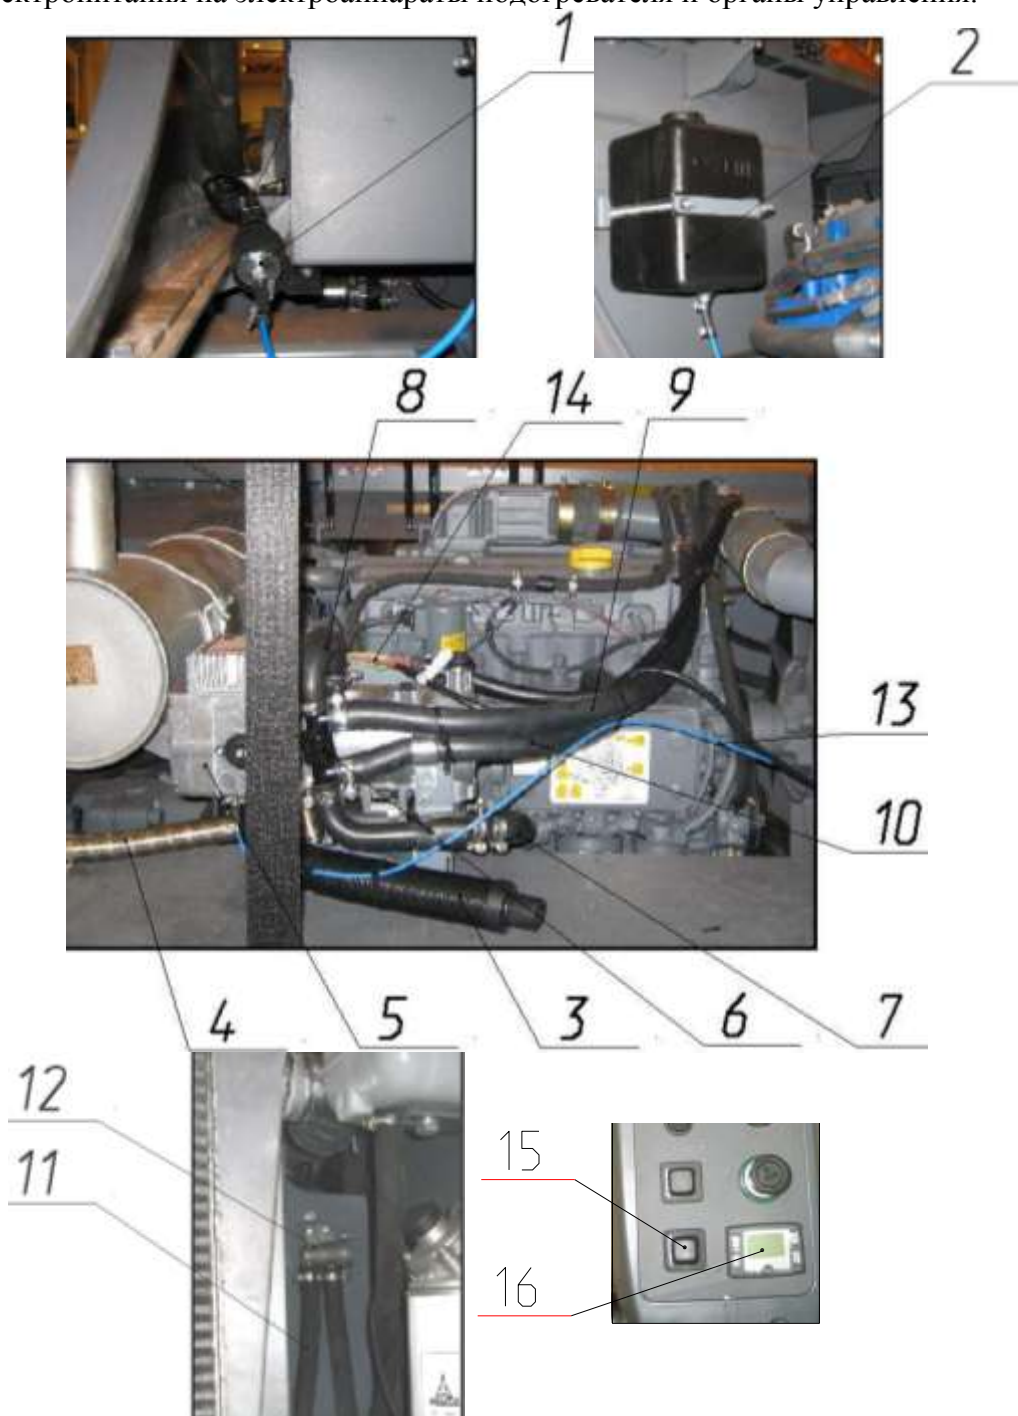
Установка предпускового подогрева двигателя.
